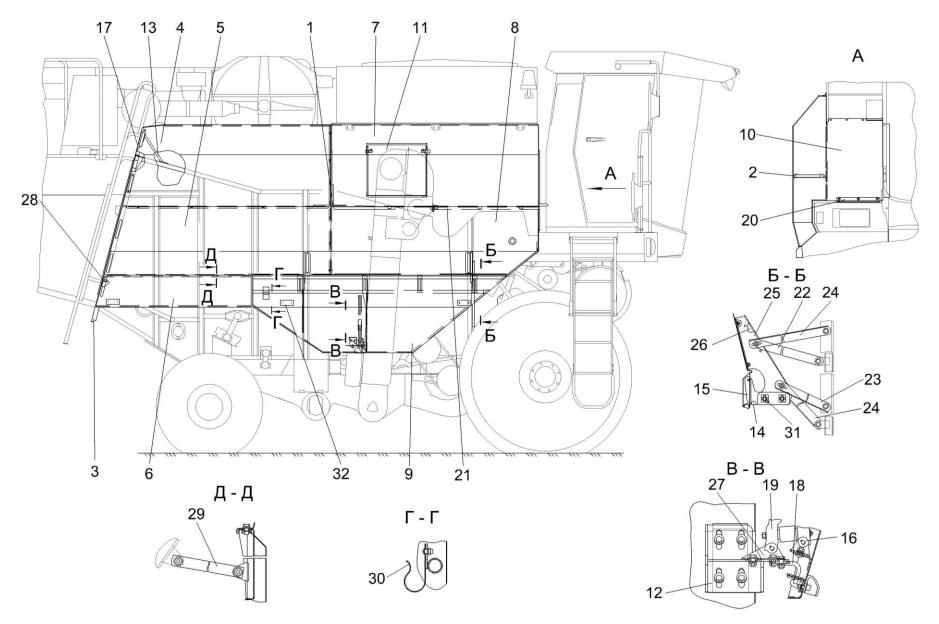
Установка капотов и ограждений КЗК-10-0128000Р2 (вид справа)
